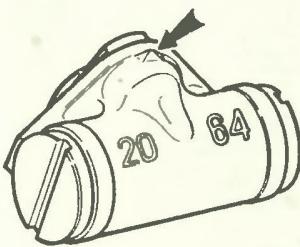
Колесный цилиндр; стрелкой показан пирамидальный выступ.
